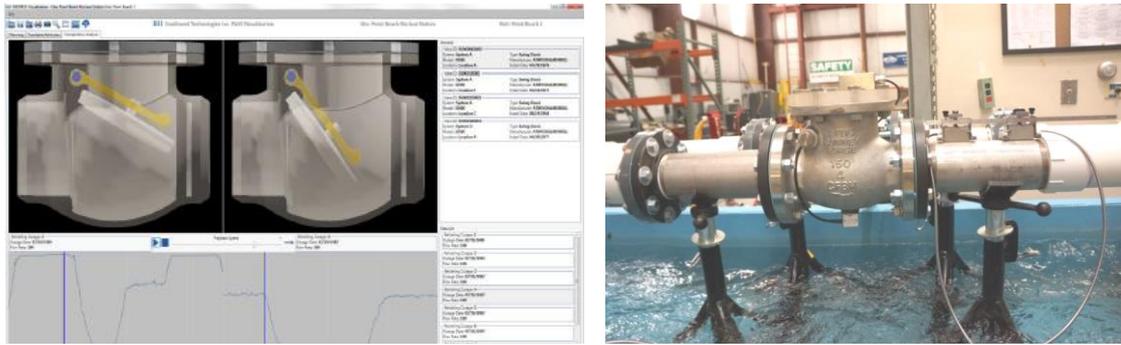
PAUT 技術應用 - Valve 營運中監視閥盤開度位置
